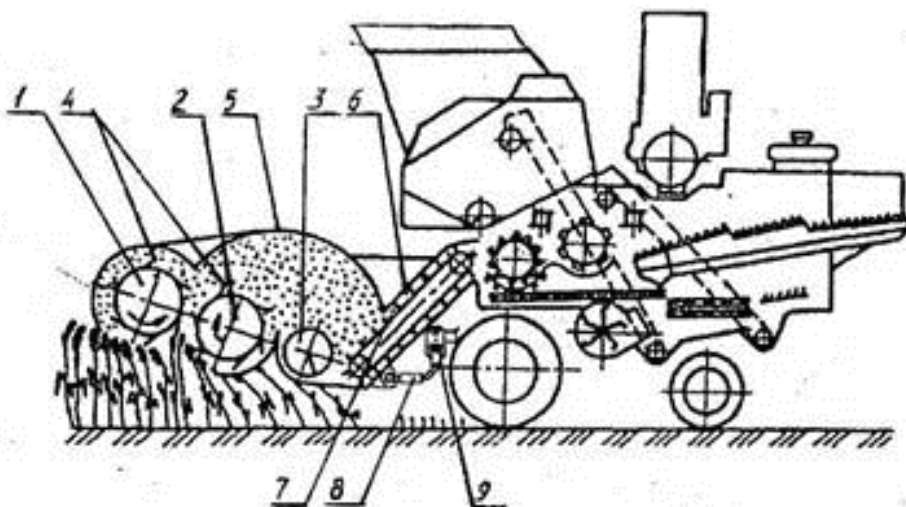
Вариант зерноуборочного комбайна с навесной очесывающей жаткой
